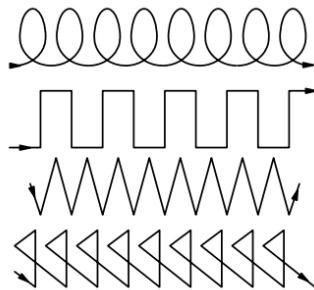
Padrões de tecimento (Modenesi – Técnica Operatória da Soldagem SMAW - 1)
